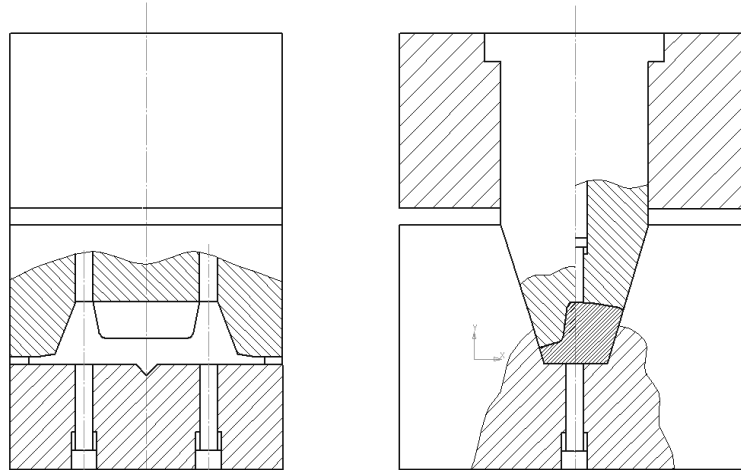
Схема чистового рівчака штампа КГШП для виготовлення сухаря з ребром жорсткості
